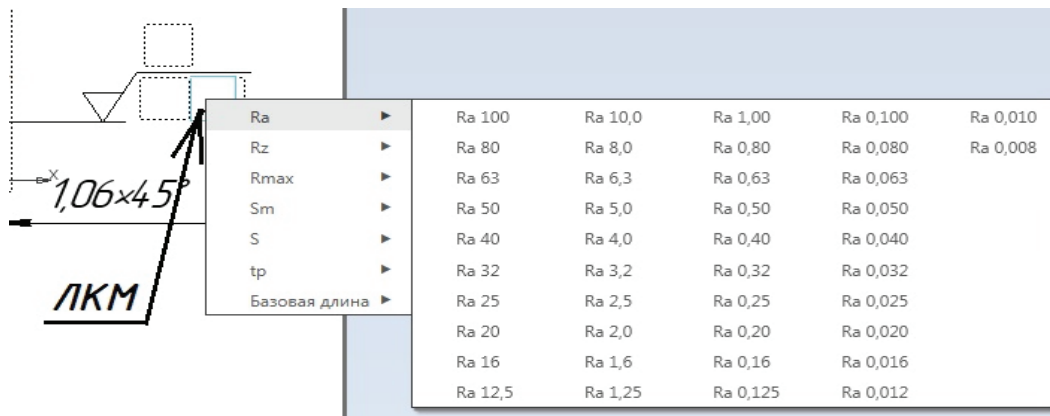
Выбор параметров шероховатости поверхности на чертеже
